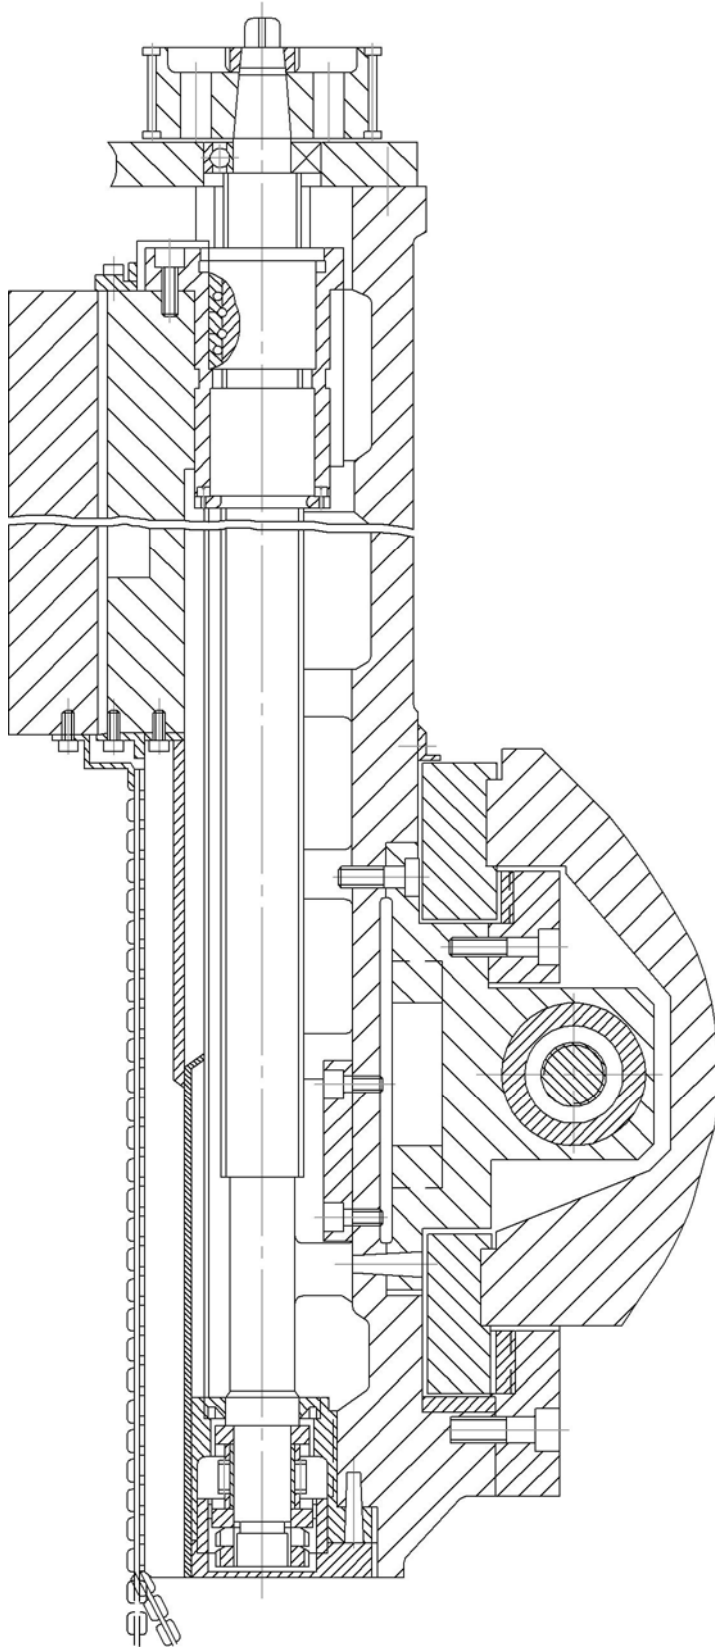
Пояснить особенности направляющих фрезерного станка с ЧПУ
